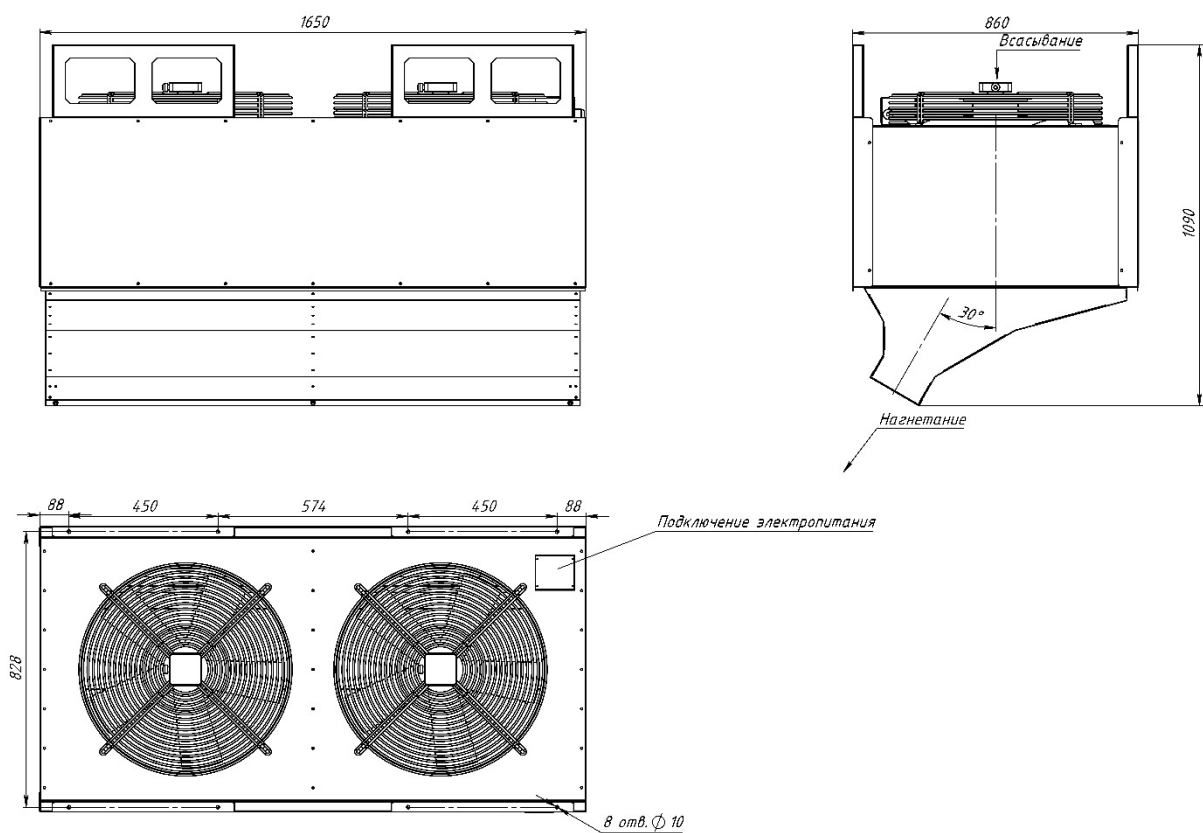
Габаритные и присоединительные размеры SA1 14000 Z (левое исполнение)
